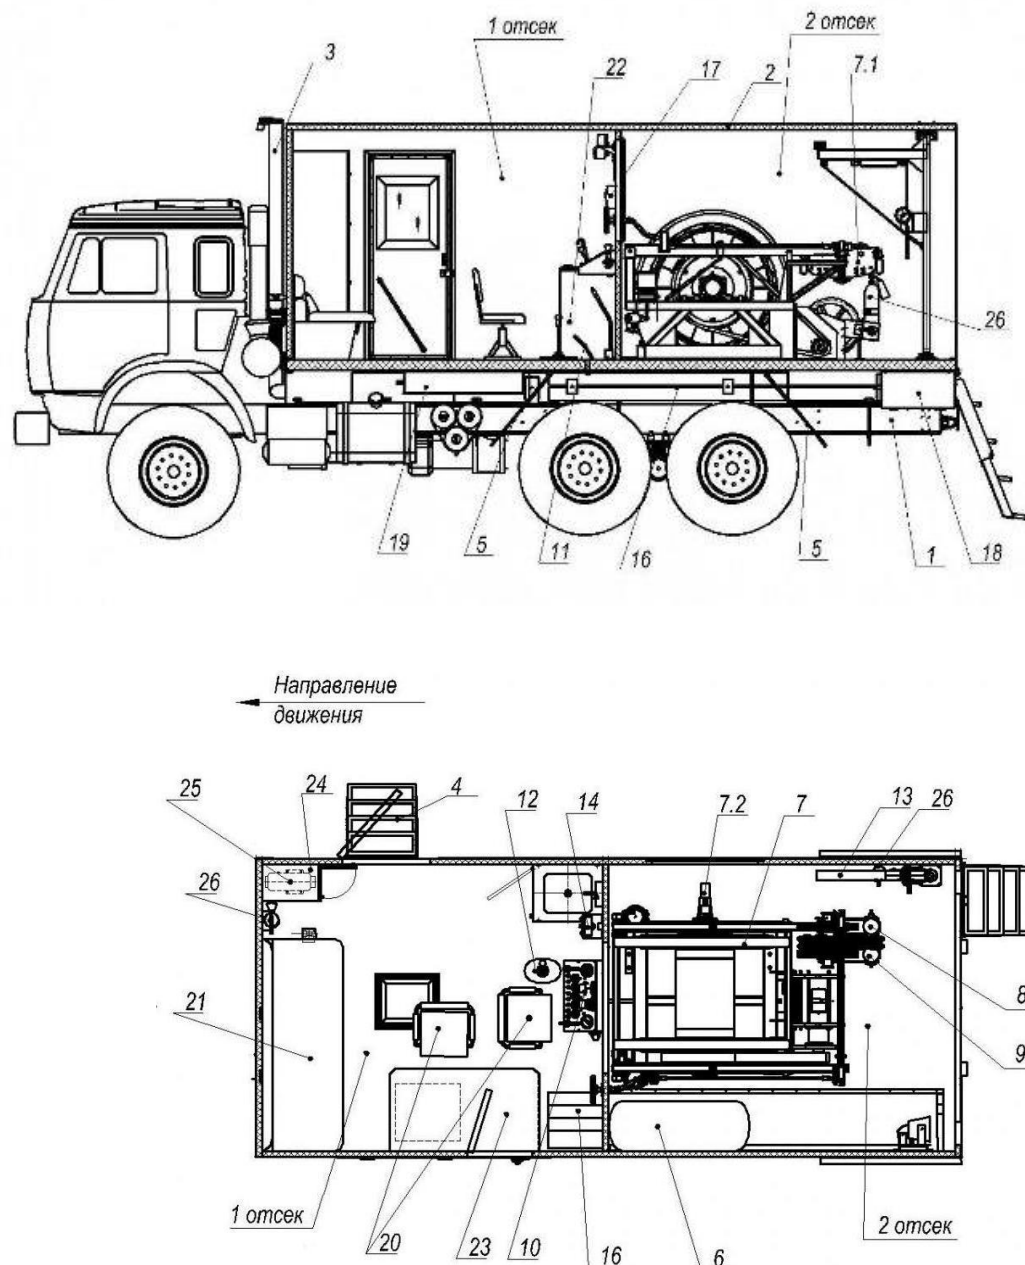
Каротажный подъемник, схема размещения оборудования:
